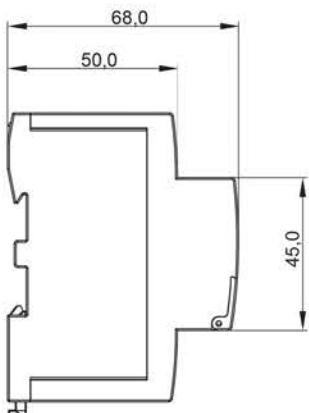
Габаритные размеры дополнительных контактов типа 1НО, 1НЗ, 2НЗ и 2НО / Figure 7 – Dimensions of auxiliary contacts of 1NO, 1NZ, 2NZ and 2NO types
